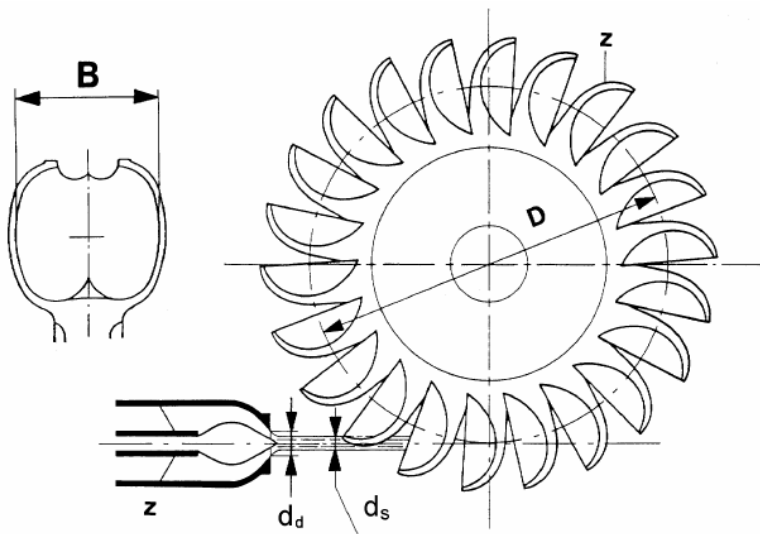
Dimensiunile principale ale rotorului turbinei Pelton
